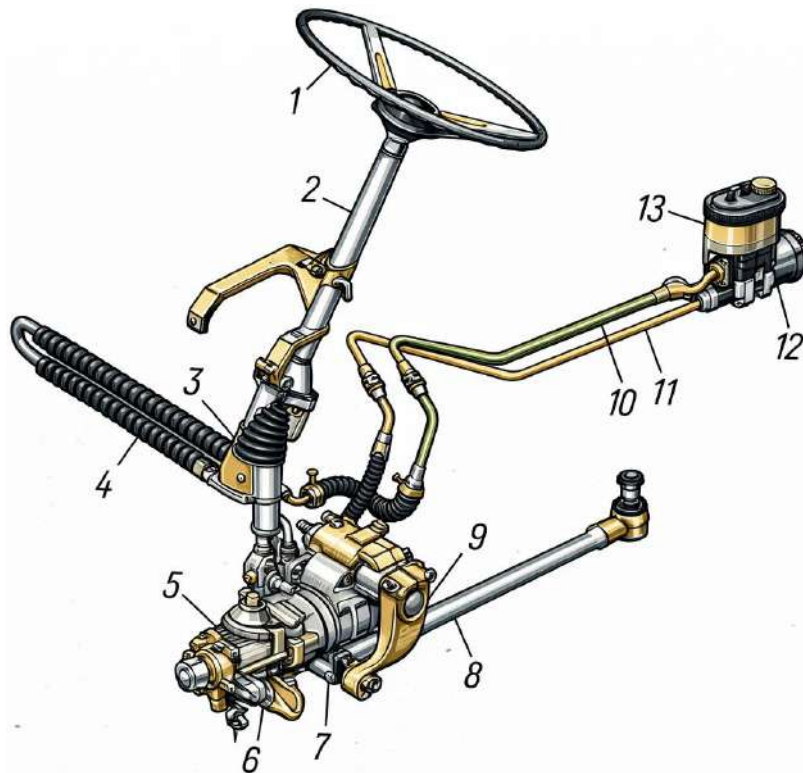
Складові рульового керування: 1 — рульове колесо; 2 — рульова колонка; 3 — карданний вал; 4 — радіатор; 5 — керуючий клапан гідропідсилювача; 6 — кутовий редуктор; 7 — рульовий механізм, об'єднаний із гідропідсилювачем; 8 — поздовжня рульова тяга; 9 — сошка; 10 — магістраль низького тиску; 11 — магістраль високого тиску; 12 — насос гідропідсилювача; 13 — бачок робочої рідини гідросистеми.
